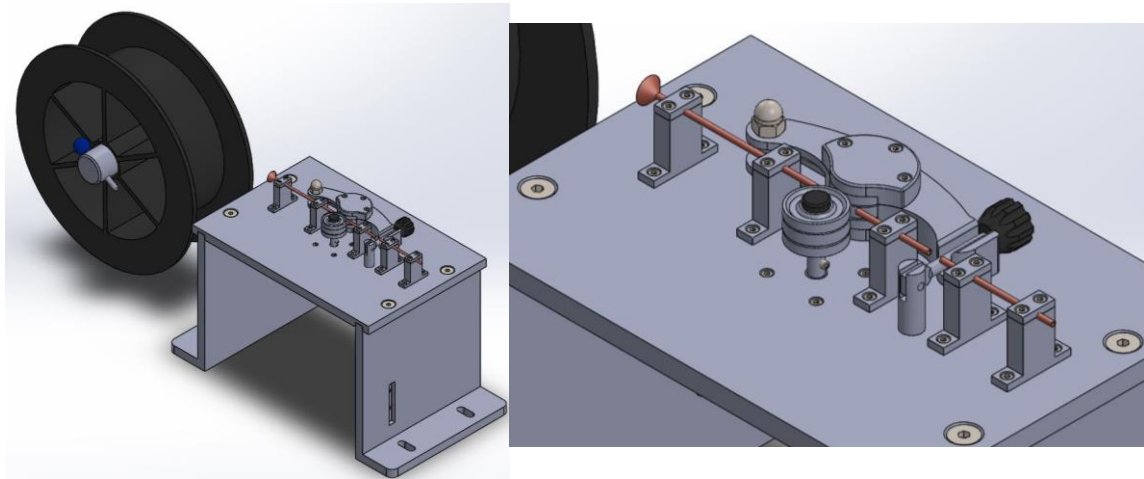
Vistas isométricas del diseño CAD del alimentador de hilo.
